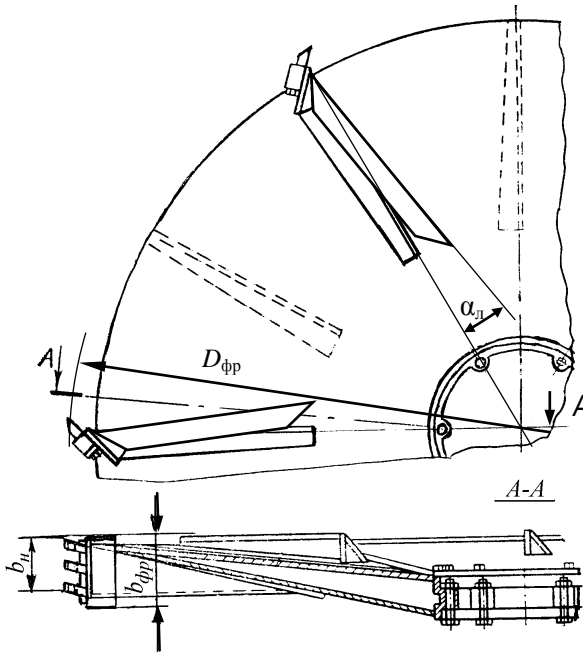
Конструкция фрезы с гребенчатыми ножами
